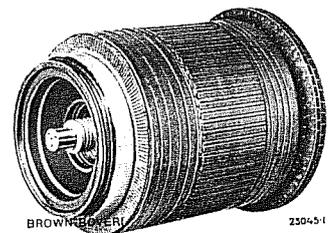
Ansicht des Rotors eines Triebmotors.
